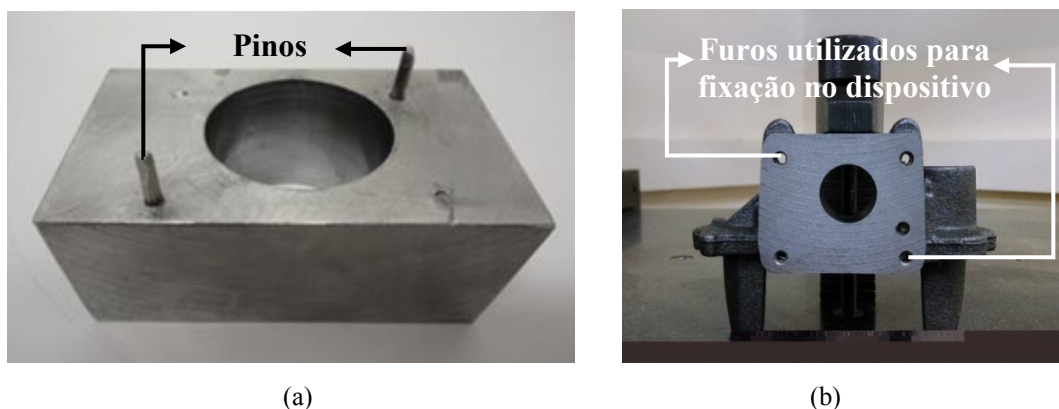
(a) Dispositivo utilizado para fixação do bloco no centro de usinagem CNC durante a realização do brunimento flexível (Fernandes, 2014) e (b) furos do bloco do compressor utilizados para fixação no dispositivo.
